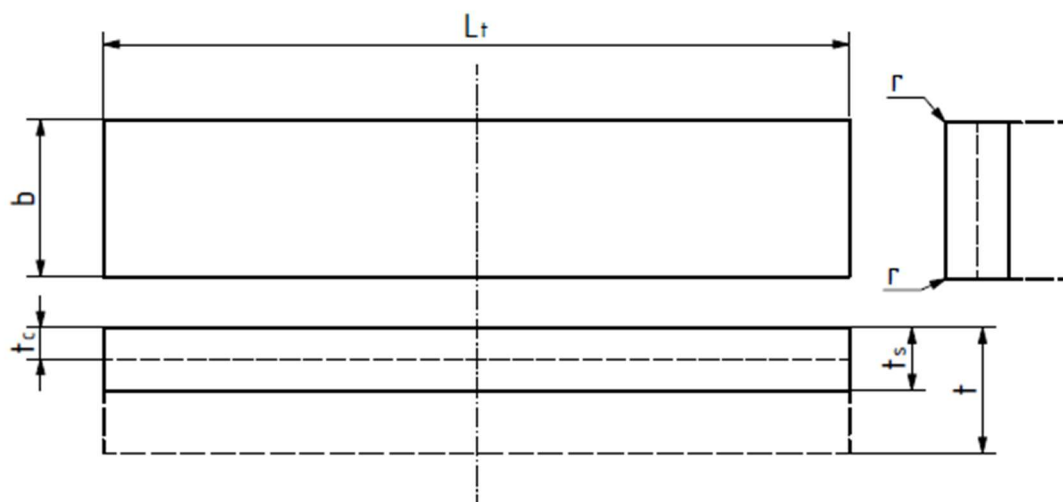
Tyč pro podélnou zkoušku ohybem tupého svaru (LFBB a LRBB) [26]
